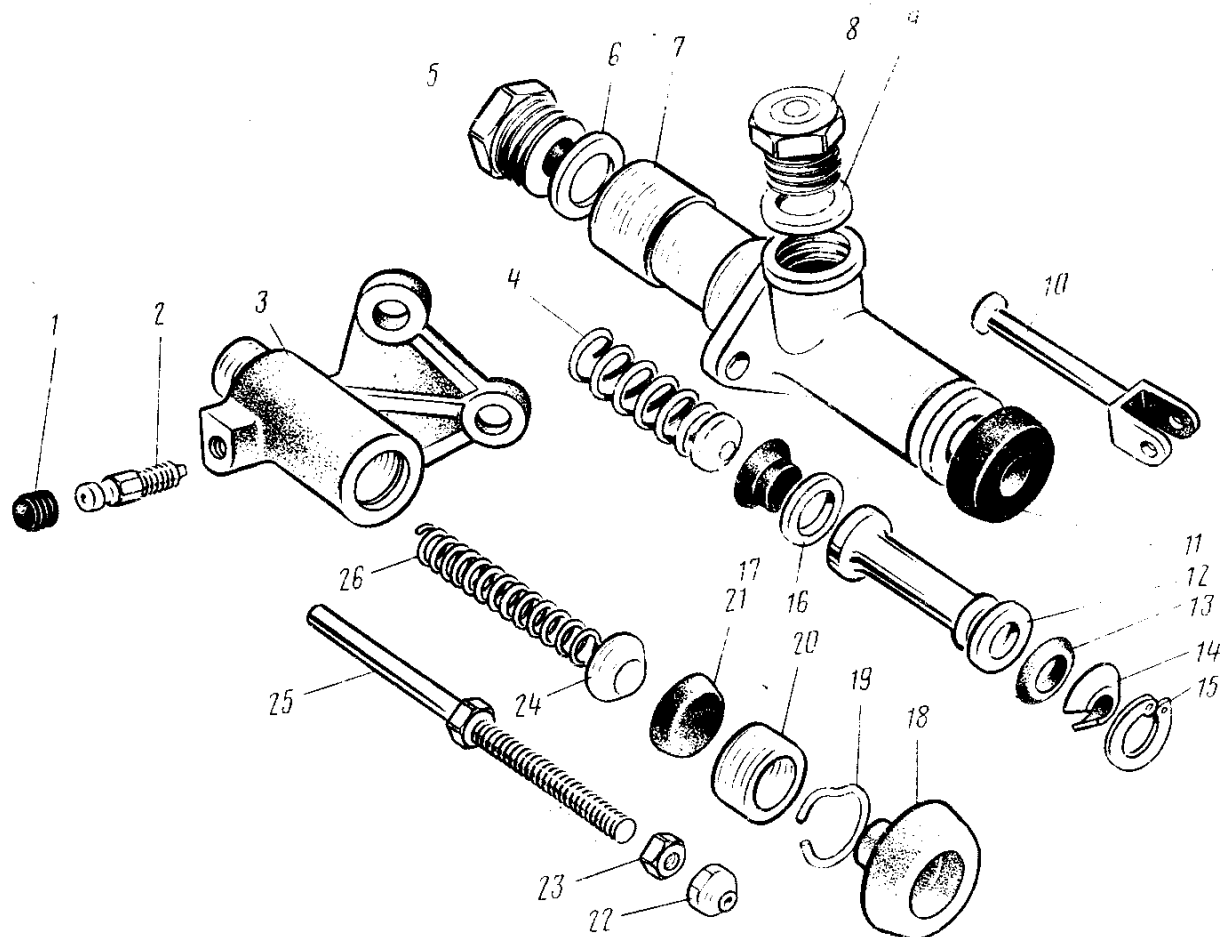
Главный и рабочий цилиндры привода выключения сцепления: 1 — колпачок; 2 — клапан; 3 — корпус рабочего цилиндра; 4 — пружина; 5 — штуцер; 6 — шайба; 7 — корпус главного цилиндра; 8 — пробка; 9 — шайба; 10 — толкатель; 11, 18 — защитные колпачки; 12 — поршень; 13 — наружная манжета; 14 — упорная шайба; 15, 19 — стопорные кольца; 16 — клапан; 17 — внутренняя манжета; 20 — поршень; 21 — уплотнительная манжета; 22 — регулировочная гайка; 23 — контргайка; 24 — распорный грибок; 25 — толкатель; 26 — пружина.
